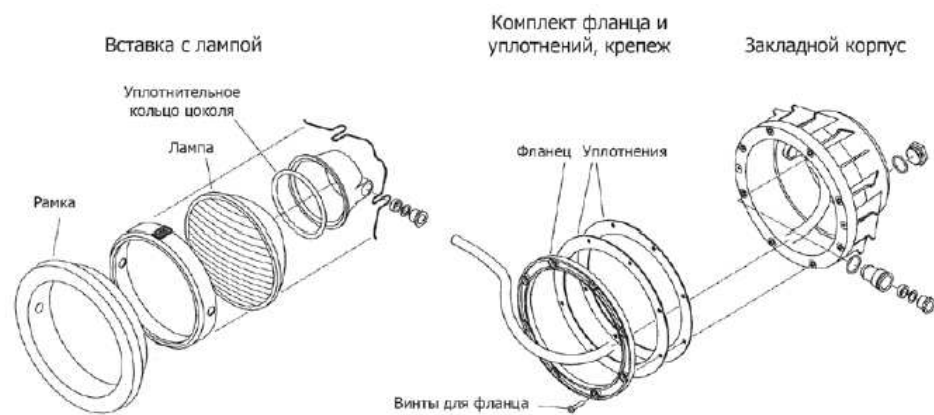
Детальная схема прожектора с закладным корпусом
